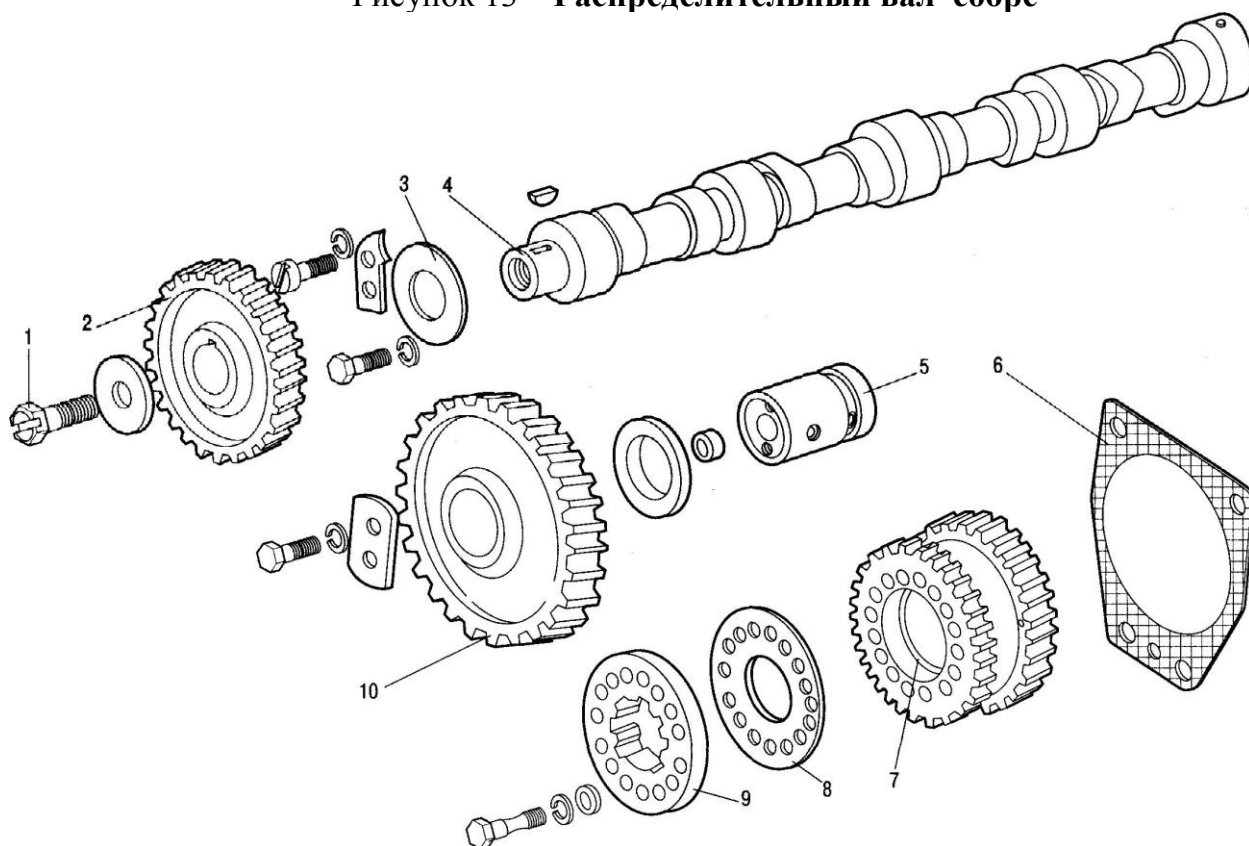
Распределительный механизм: 1 - болт; 2 - шестерня привода распределительного вала; 3 - шайба; 4 - распределительный вал; 5 - палец; 6 - прокладка; 7 - шестерня привода топливного насоса высокого давления; 8 - упорное кольцо; 9 - фланец; 10 - промежуточная шестерня
